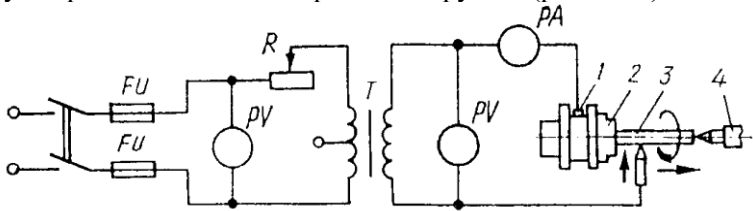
Принципова схема ЕМО: 1 – струмознімна щітка; 2 – патрон; 3 – деталь; 4 – задня бабка
